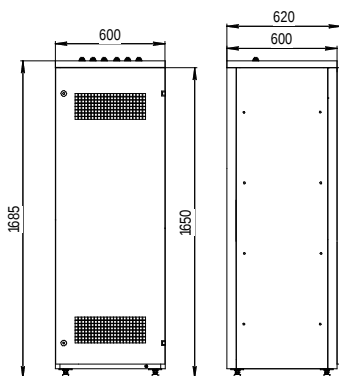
Габаритный чертеж шкафа аккумуляторного УЭПС-2 А3
